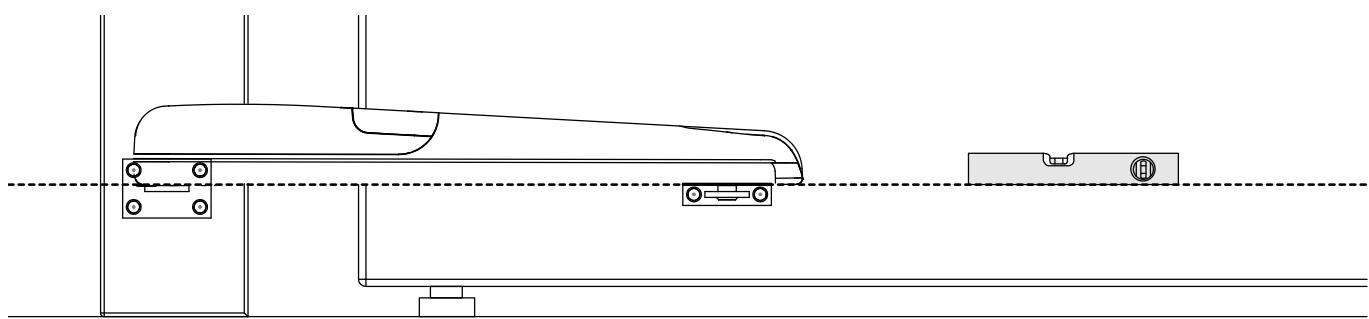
FR - Fixation du motoréducteur et du chevron arrière
